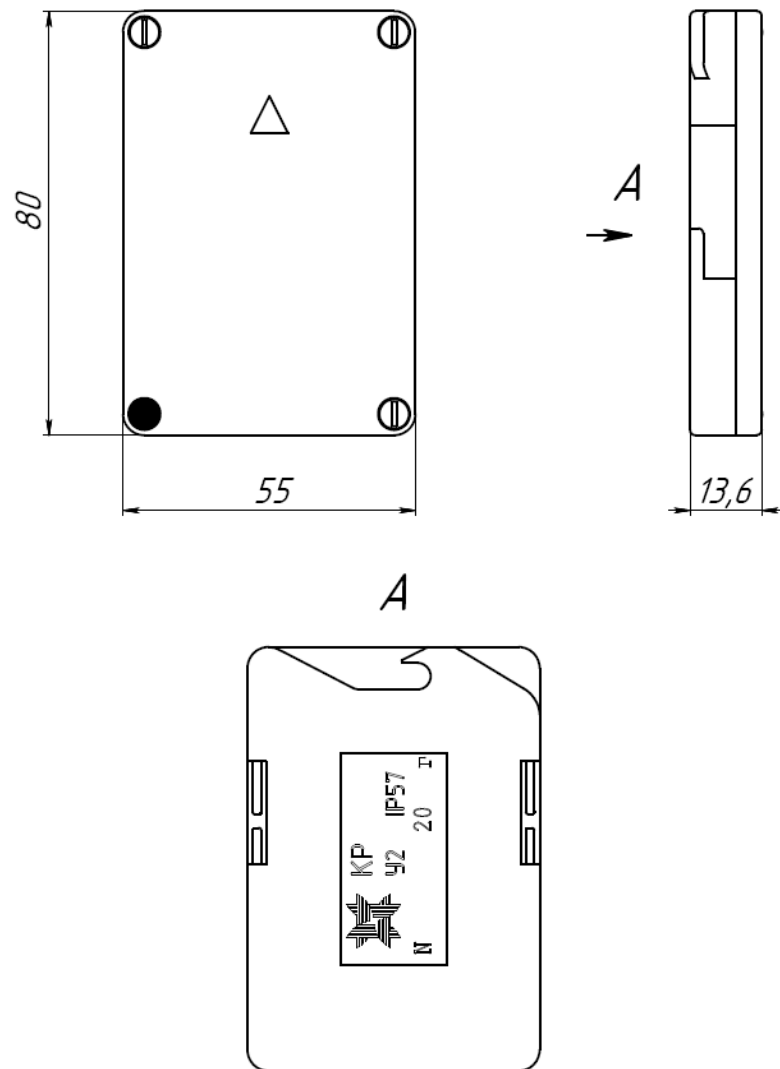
Внешний вид и габаритные размеры кассеты регистрации КР 36993-360-00
